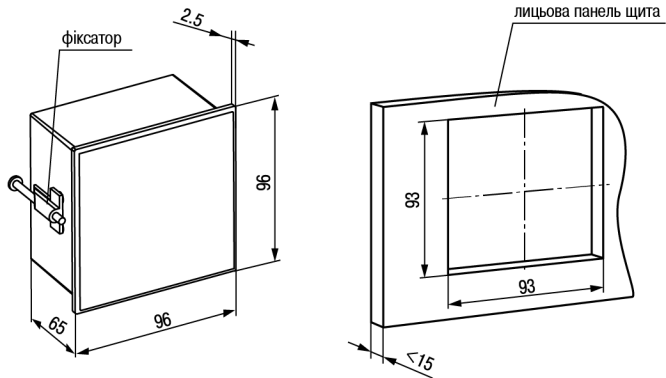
Габаритні розміри корпусу Щ1
